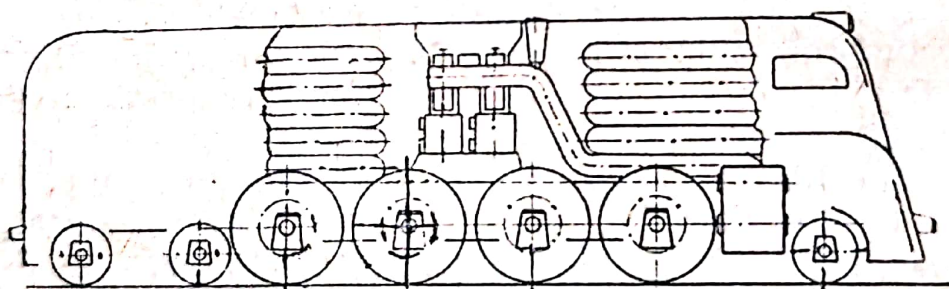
Locomotivă acționată prin generatoare de gaze cu pistoane libere. Combustibil — gaz metan (locomotivă cu abur, veche, transformată).
